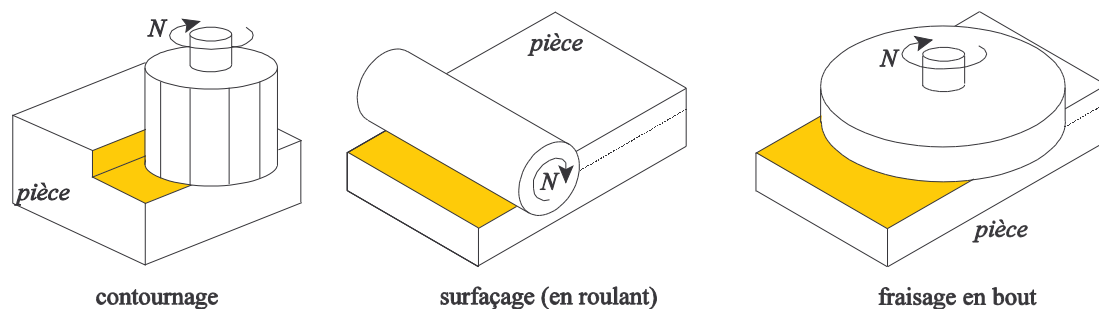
opérations de fraisage; les surfaces usinées sont coloriées en jaune
